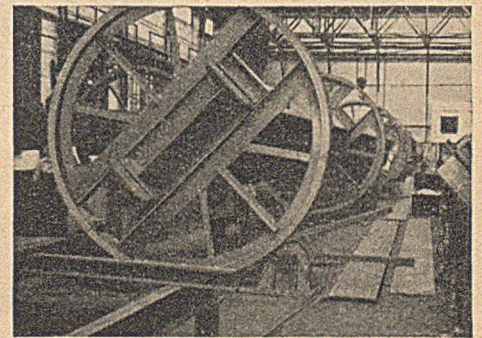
Drehvorrichtung für die Schweißung der kurzen Nähte an den Stützen.
